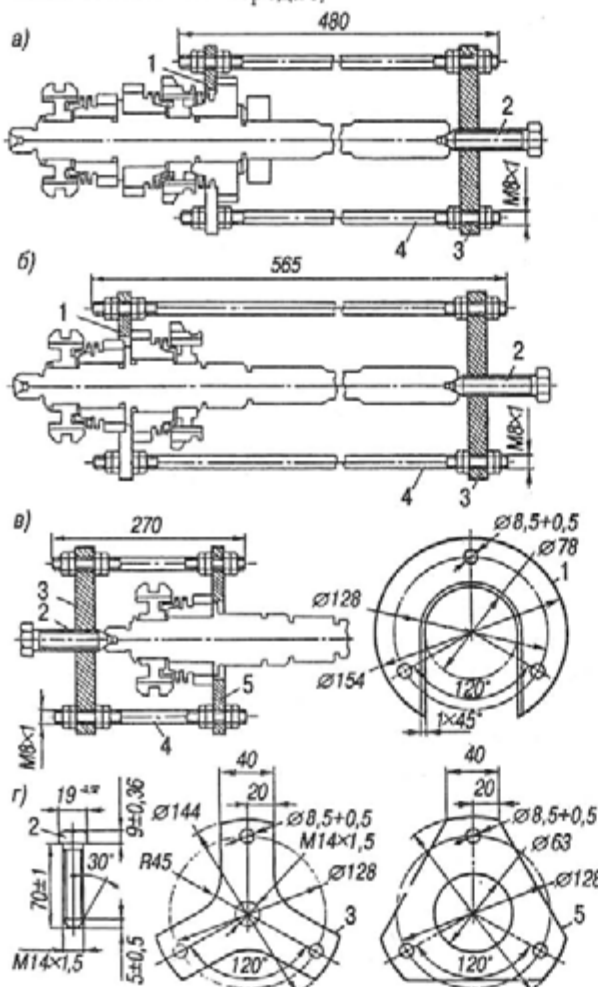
Приспособление для разборки вторичного вала: а) демонтаж подшипника вторичного вала; б) демонтаж ступицы синхронизатора включения 1-ой и 2-ой передач; в) демонтаж ступицы синхронизатора включения 3-ей и 4-ой передач; г) шайбы. 1 - средняя пластина; 2 - болт; 3 - задняя пластина; 4 - шлицы; 5 - передняя пластина
